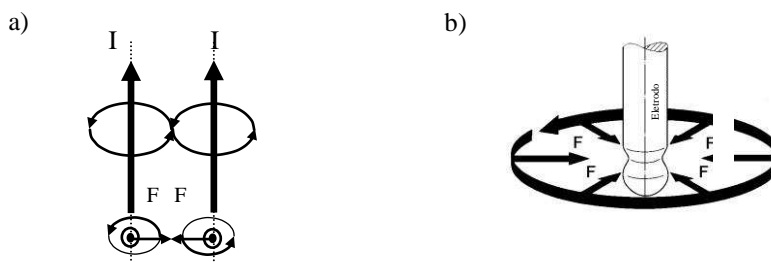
Efeito Pinch a) dois fios onde passa a corrente na mesma direção e b) eletrodo de soldagem com efeito de estrangulamento [56]
